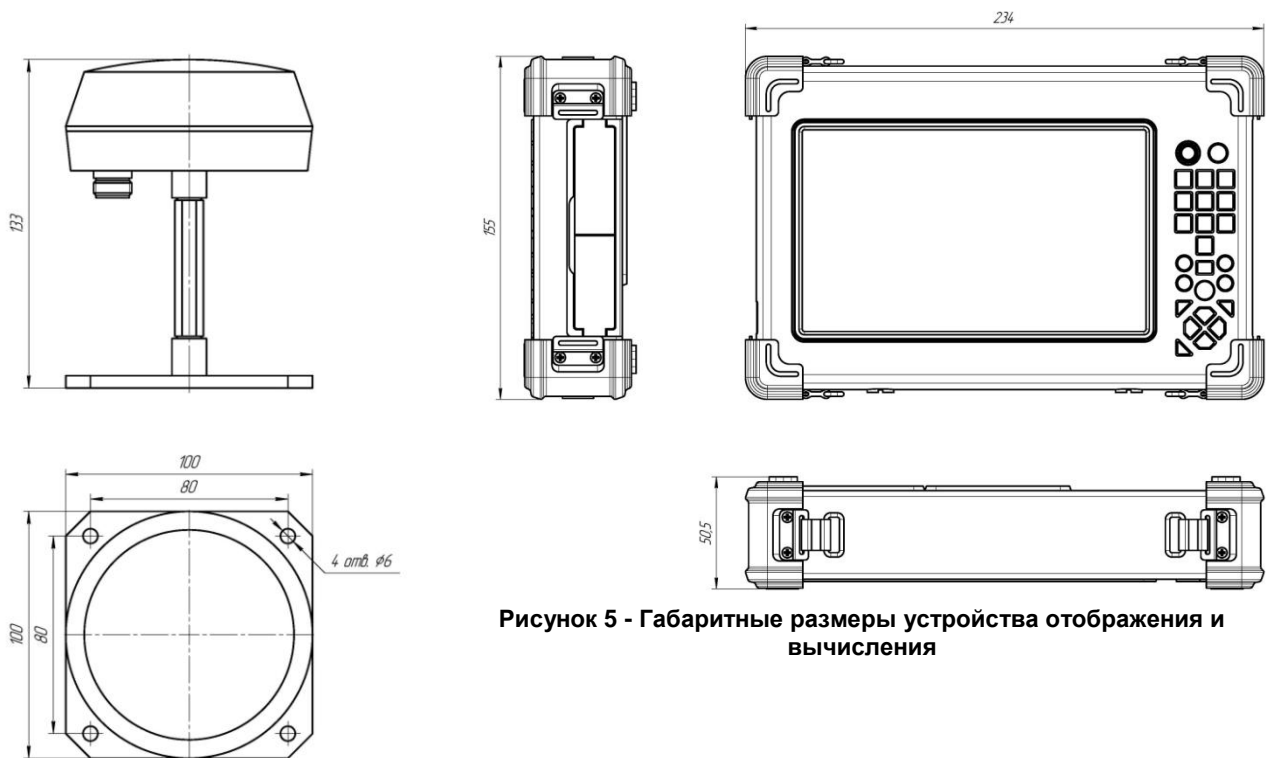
Габаритные размеры устройства отображения и вычисления
